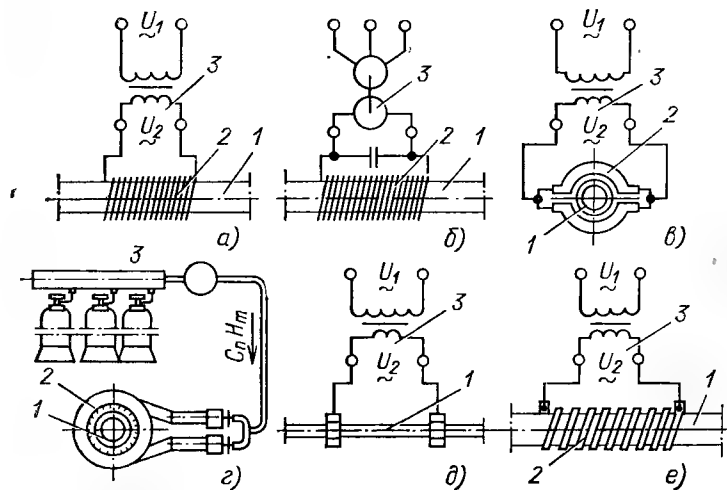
Способы нагрева при местной термической обработке сварных соединений труб.
